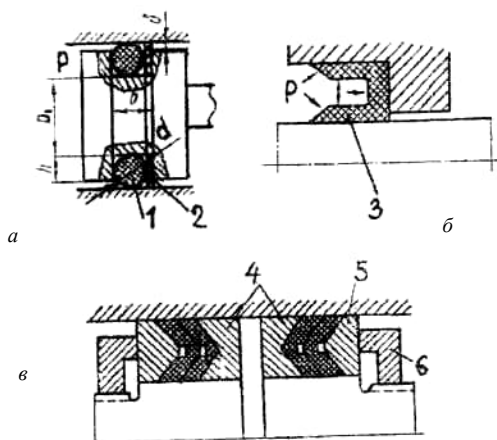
Уплотнения подвижных соединений гидроцилиндров: а) кольцевое уплотнение; б) U-образная манжета; в) V-образная манжета: 1 – кольцо резиновое; 2 – шайба предохранительная; 3 – манжета; 4 – кольцо опорное; 5 – кольцо распорное; 6 – гайка
